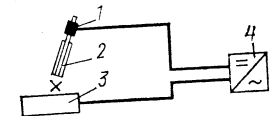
Принцип сварки: 1 — электрододержатель с кабелем; 2 — обмотанный сварочный электрод; 3 — изделие с кабелем; 4 — источник питания
